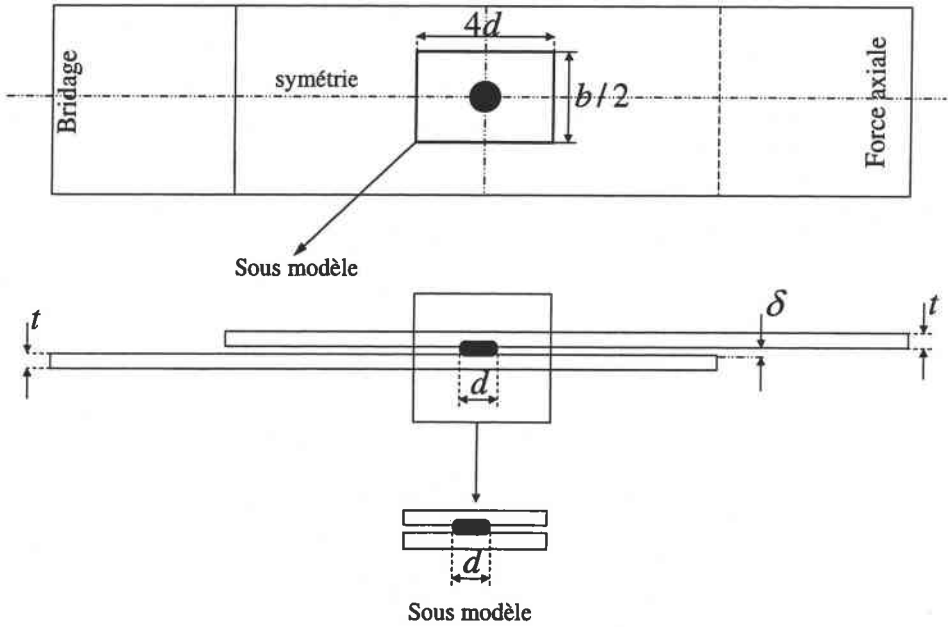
Schéma du sous modèle d'une éprouvette soudée par point Mono Point.
